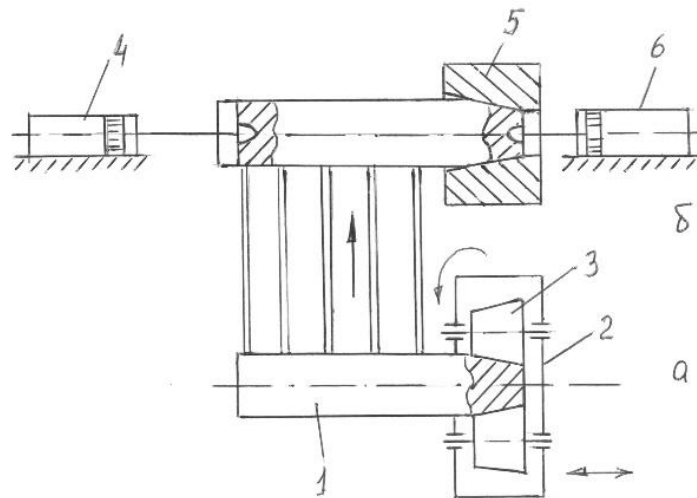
Схематичний вид установки для підготовки заготовки до прошивання: а) перша позиція; б) друга позиція; 1 — заготовка; 2 — обойма; 3 — холості ролики; 4 — гідроциліндр заштовхувача заготовок; 5 — матриця; 6 — гідроциліндр переміщення бойка
